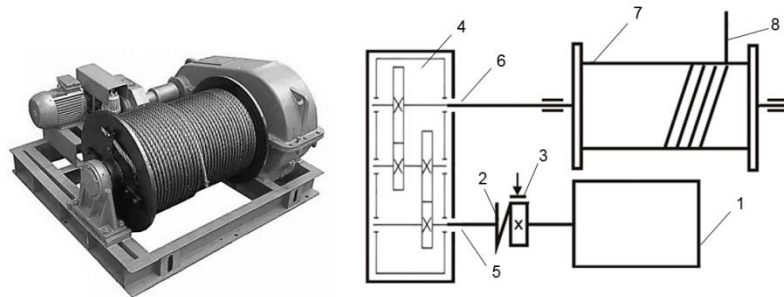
Внешний вид (слева) и кинематическая схема (справа) реверсивной электрической лебедки с цилиндрическим редуктором: 1-электродвигатель; 2-муфта; 3-тормоз; 4-редуктор; 5-быстроходный вал редуктора; 6-тихоходный вал редуктора, 7-барабан, 8-канат
